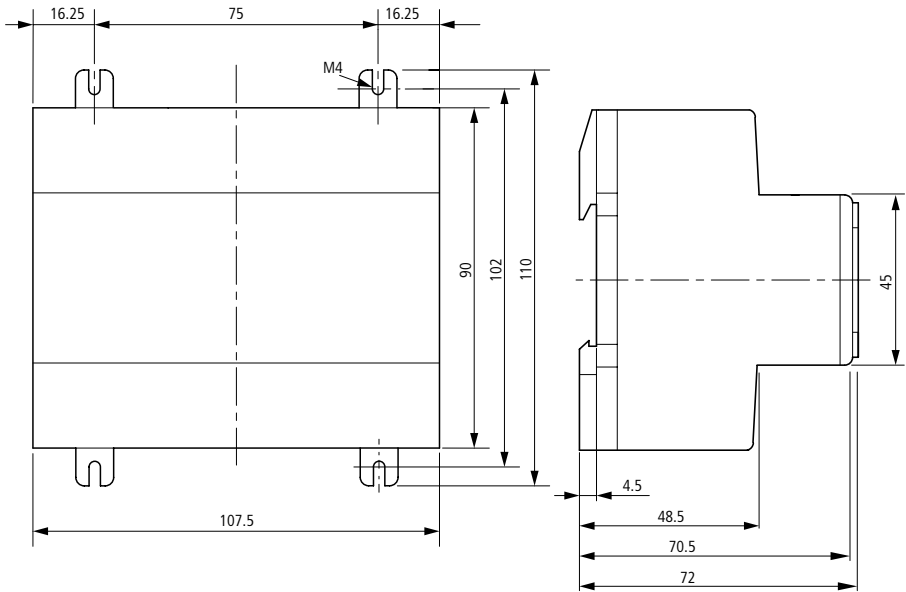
Dimensiones easy800 en mm (en pulgadas → Tabla 9)
